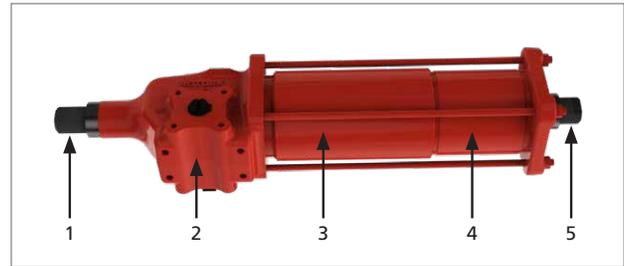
CPIS (055-065) Hauptkomponenten
